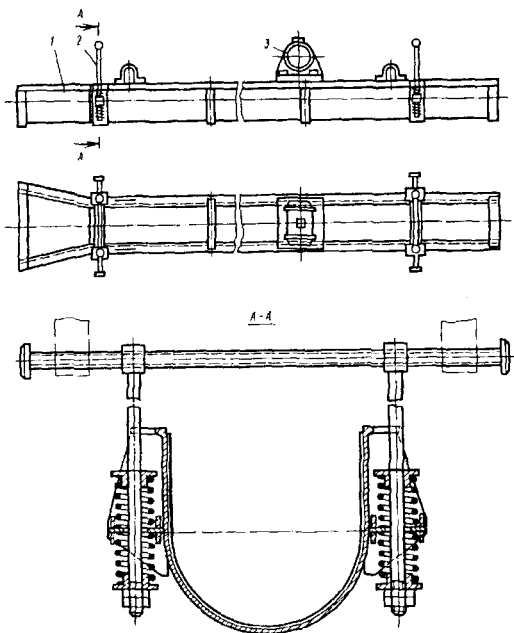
Вибрационный желоб: 1 — корпус; 2 — подвеска; 3 — вибратор.
